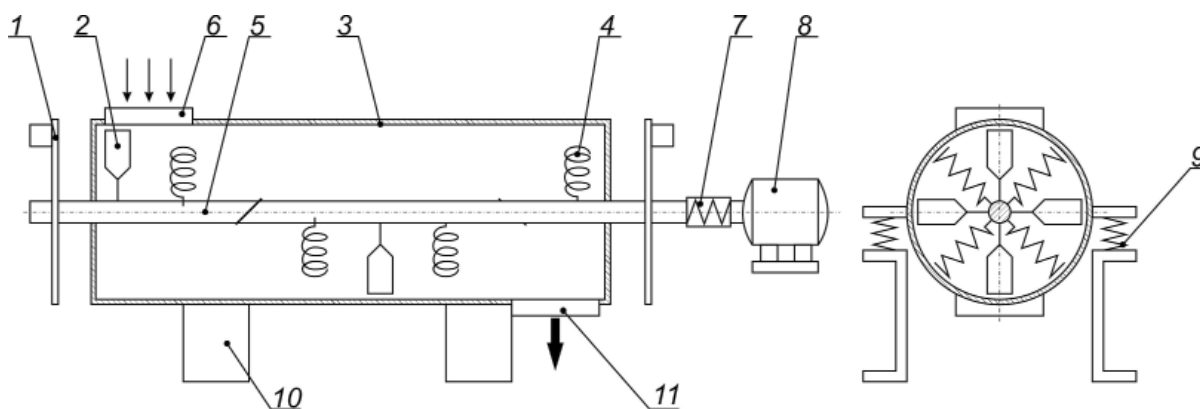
Универсальный вибросмеситель: 1 – вибровозбудитель; 2 – лопатка; 3 – контейнер; 4 – пружина; 5 – вал; 6 – загрузочная горловина; 7 – упругая муфта; 8 – приводная станция; 9 – опора; 10 – рама; 11 – выгрузной патрубок
